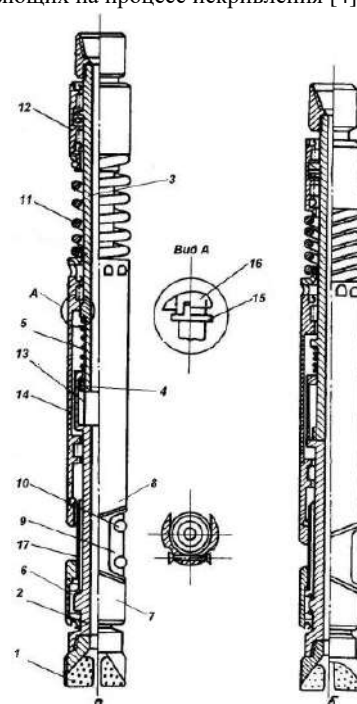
Общий вид отклонителя ТЗ-3: а – транспортное положение; б – рабочее положение; 1 – долото; 2 – нижний вал; 3 – верхний вал; 4, 13 – шлицевое соединение; 5 – роторная пружина; 6 – нижний подшипниковый узел; 7 – нижний полуклин; 8 – верхний полуклин; 9 – подвижной клин-ползун; 10 – каретка с катками; 11 – статорная пружина; 12 – верхний подшипниковый узел; 14 – корпус; 15 – блокировочный фиксатор; 16 – блокировочная муфта; 17 – трубка
